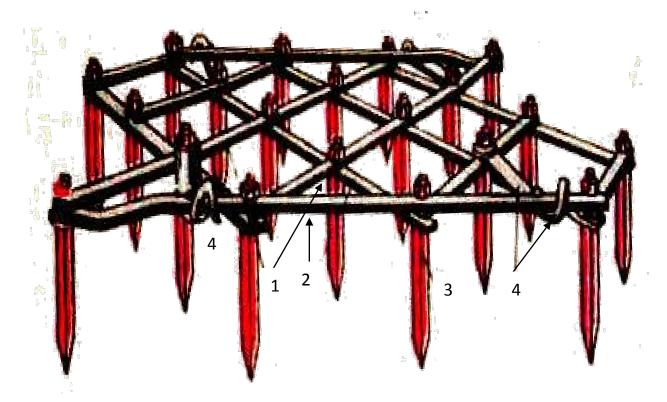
Бороны: а – БЗТС -1,0; 1, 2 – планки рамы; 3 – зуб; 4 – прицепное устройство.
